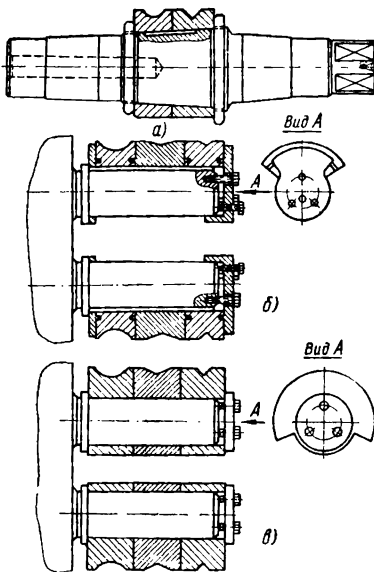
Наиболее распространенные схемы крепления штампов на валках: а — крепление набора бандажей на валок; б — крепление набора секторов; в — крепление набора бандажей на консоль валка
